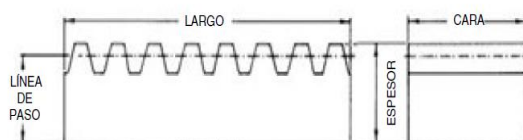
Dimensiones de la cremallera, Martin Sprocket & Gear, INC.,2017, El gran catálogo 4000.
